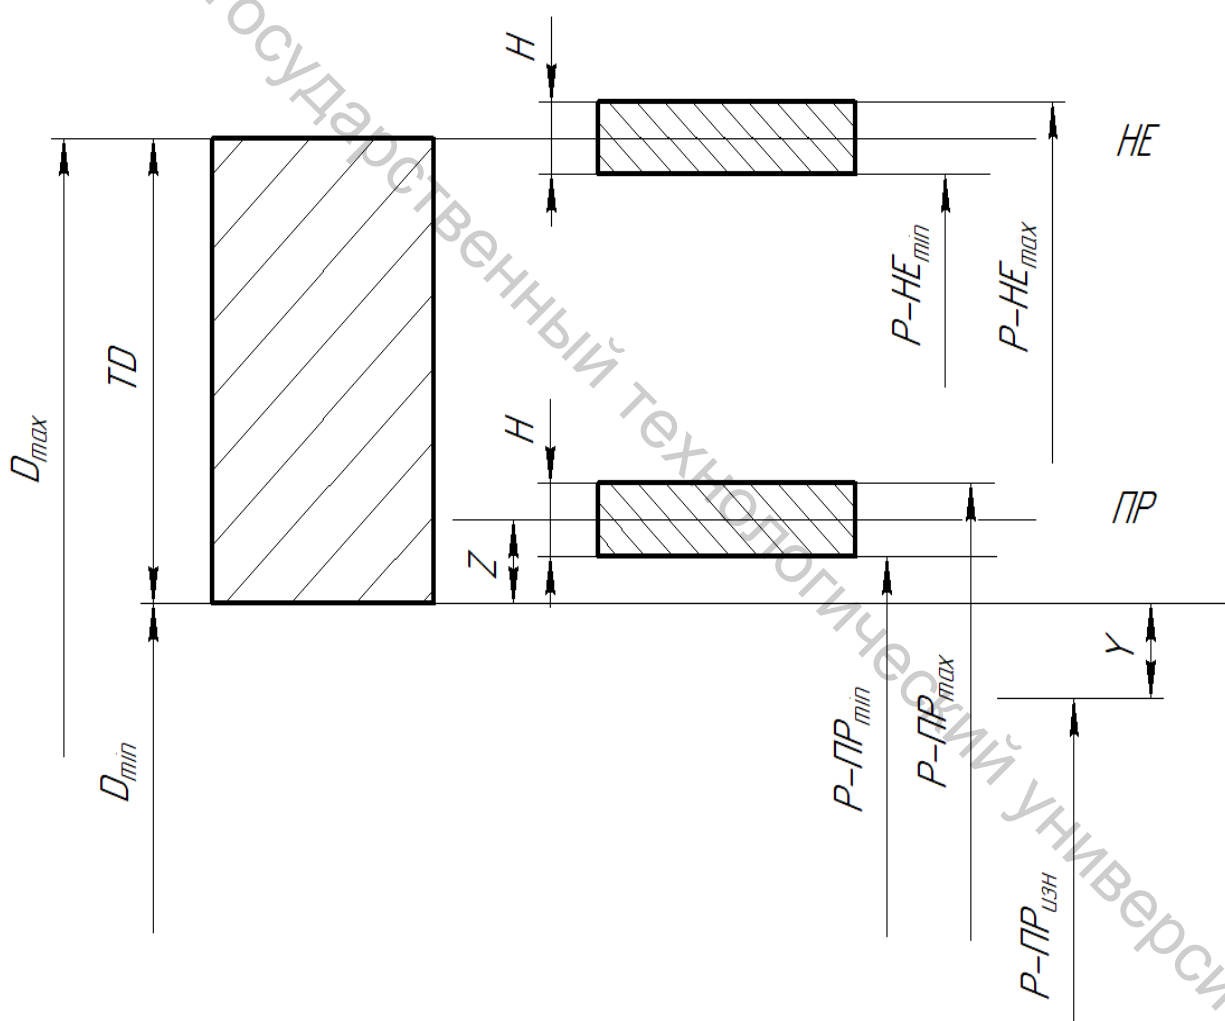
Схема расположения интервалов допусков рабочих калибров-пробок для размеров до 180 мм
